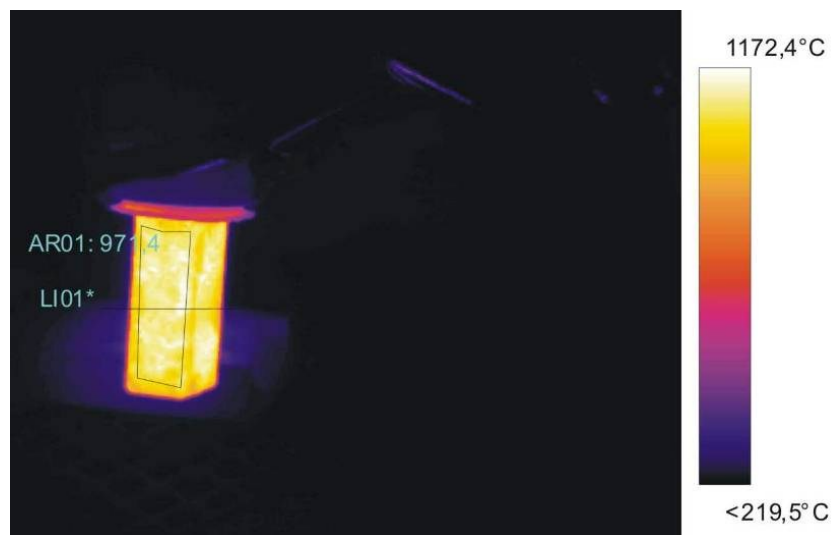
Thermobild des Gussblocks unmittelbar nach dem Strippen
